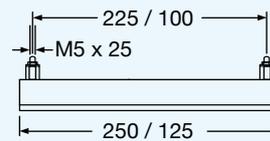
Metallzubehör, Einbaumaße und Abmessungen in mm
